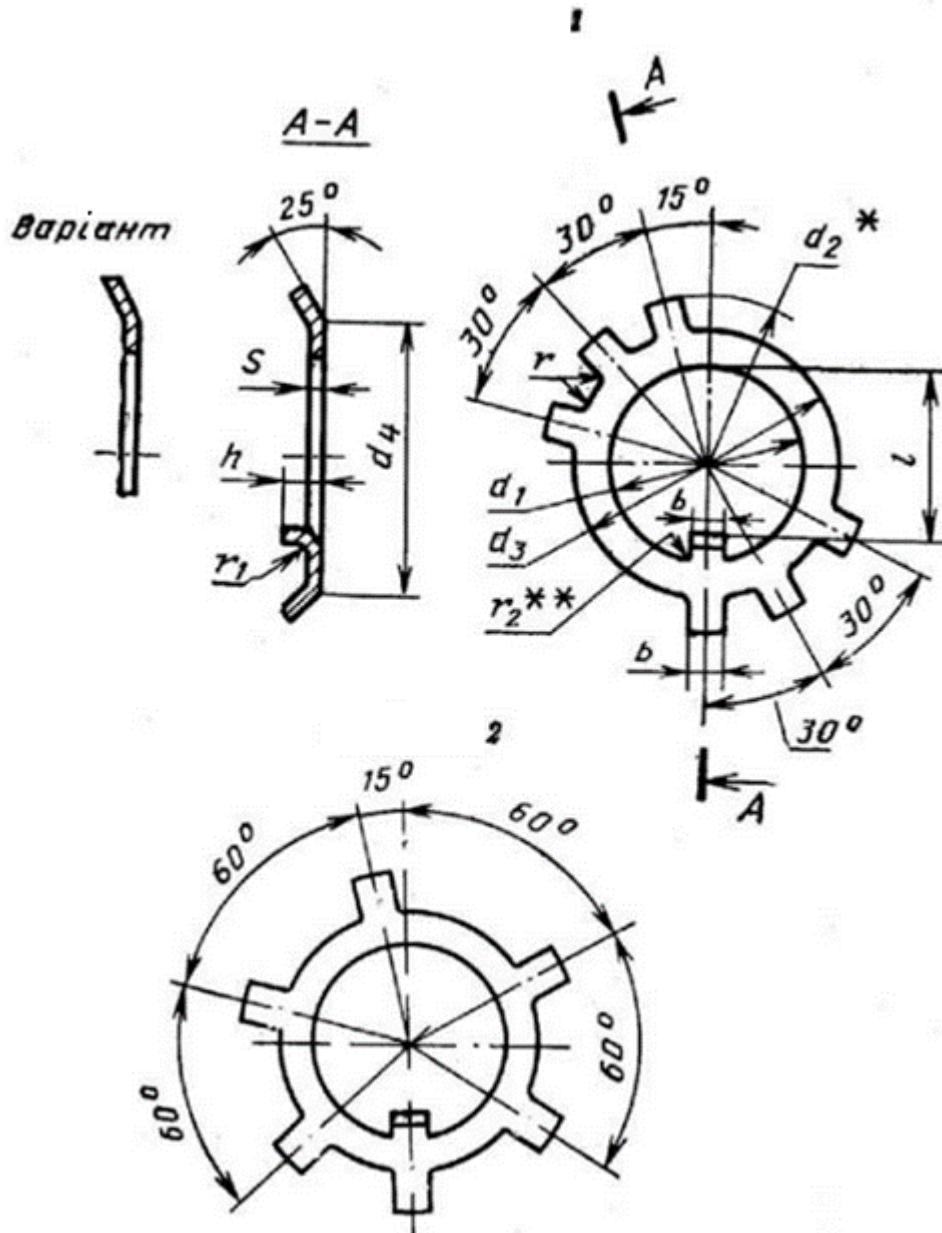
Шайба стопорна багатолапова згідно з ГОСТ 11872-89
